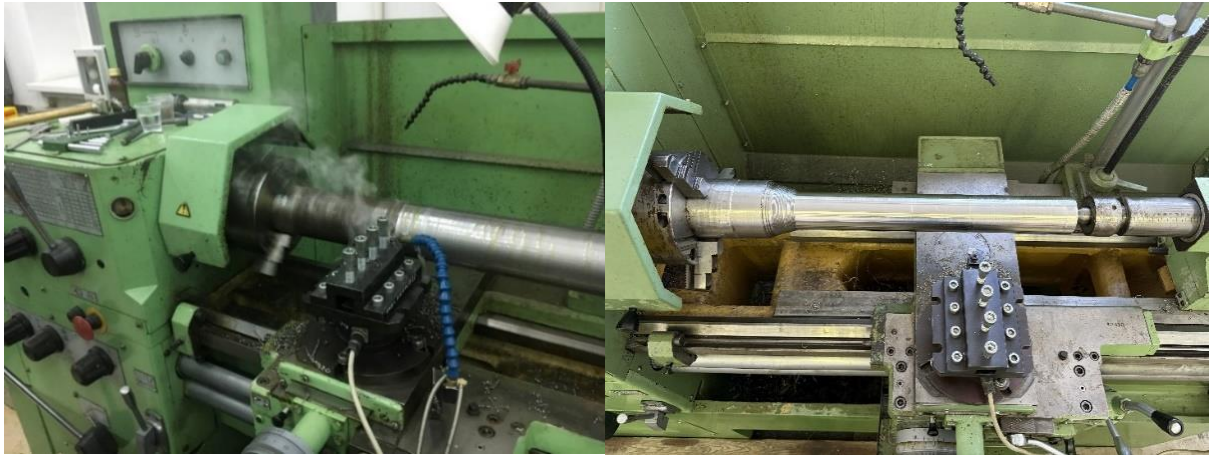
Экспериментальная установка на базе токарного станка SAMAT – 400М
